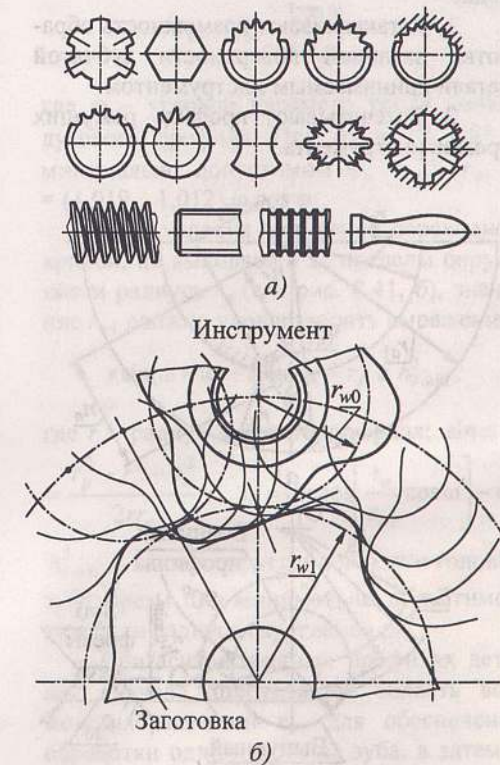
Обработка фасонных деталей обкатными инструментами: а – виды изделий, обрабатываемых обкатными инструментами; б – схема обкатной обработки по методу огибания
